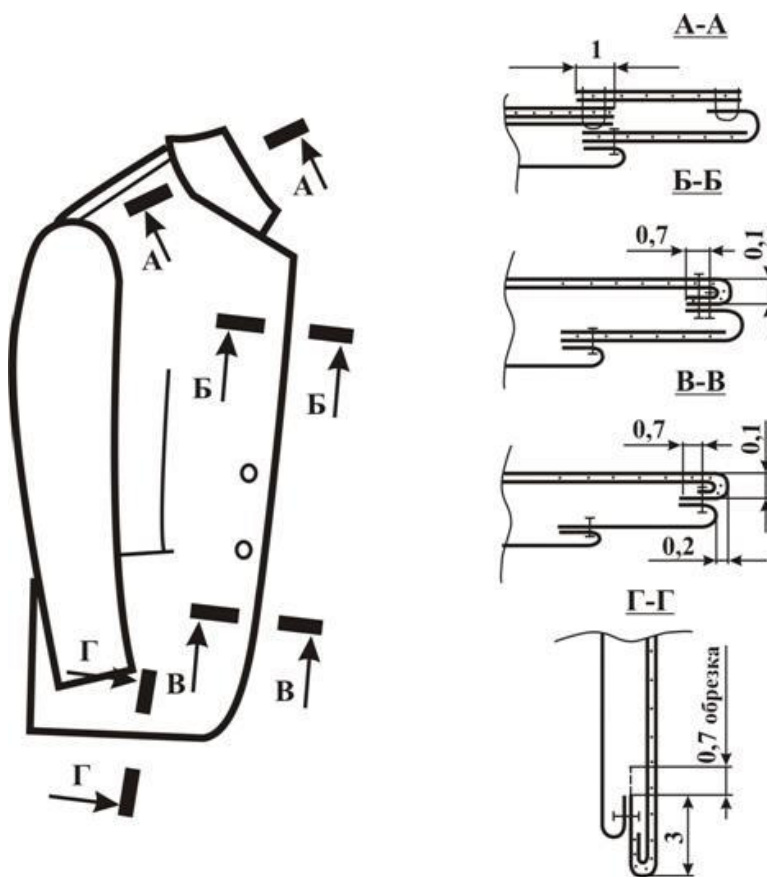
Сборочный чертеж мужского пиджака
